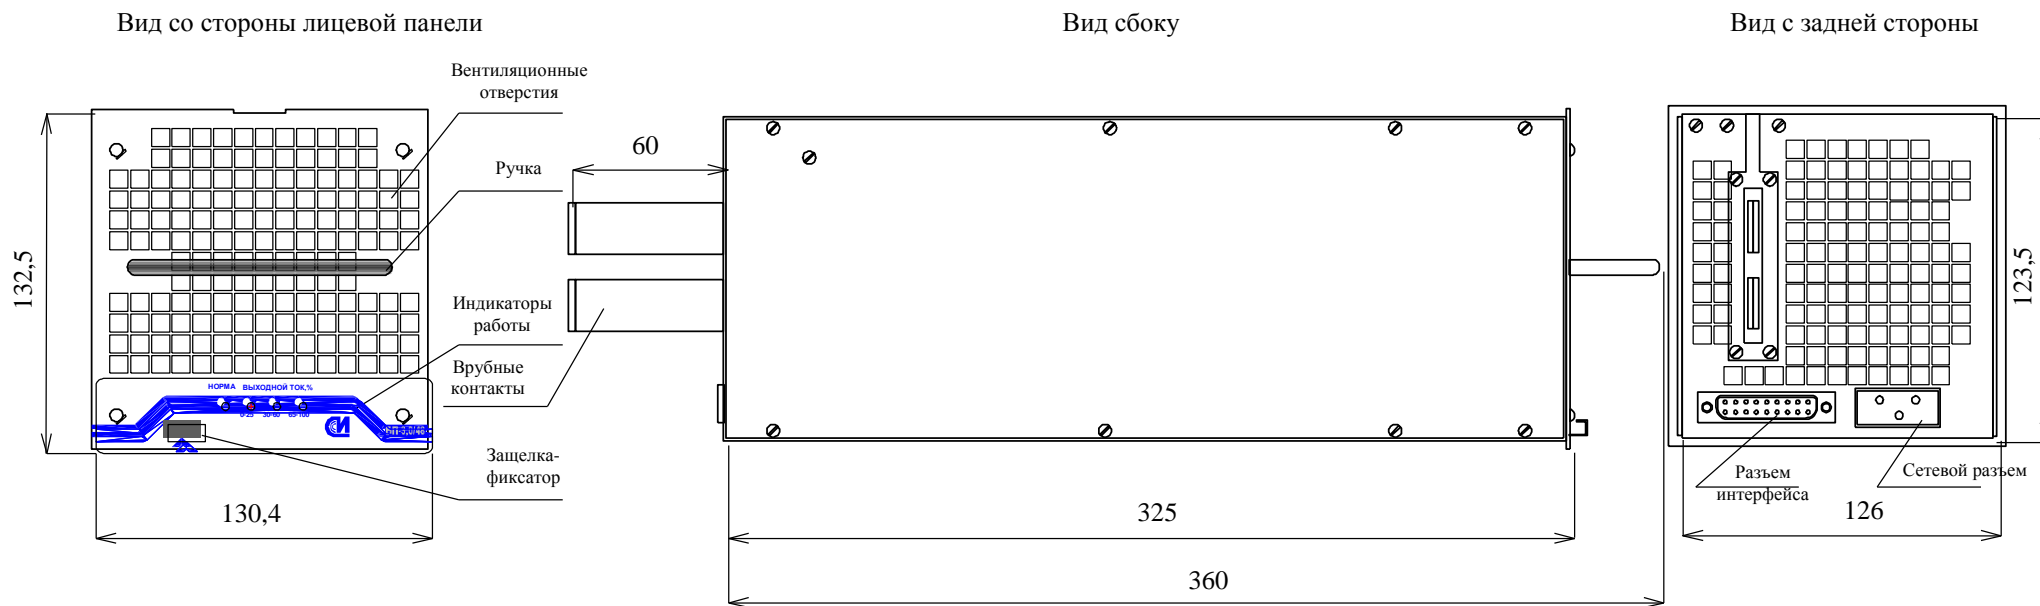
Блок питания БП-3,0/48М. Общий вид и габаритные размеры
